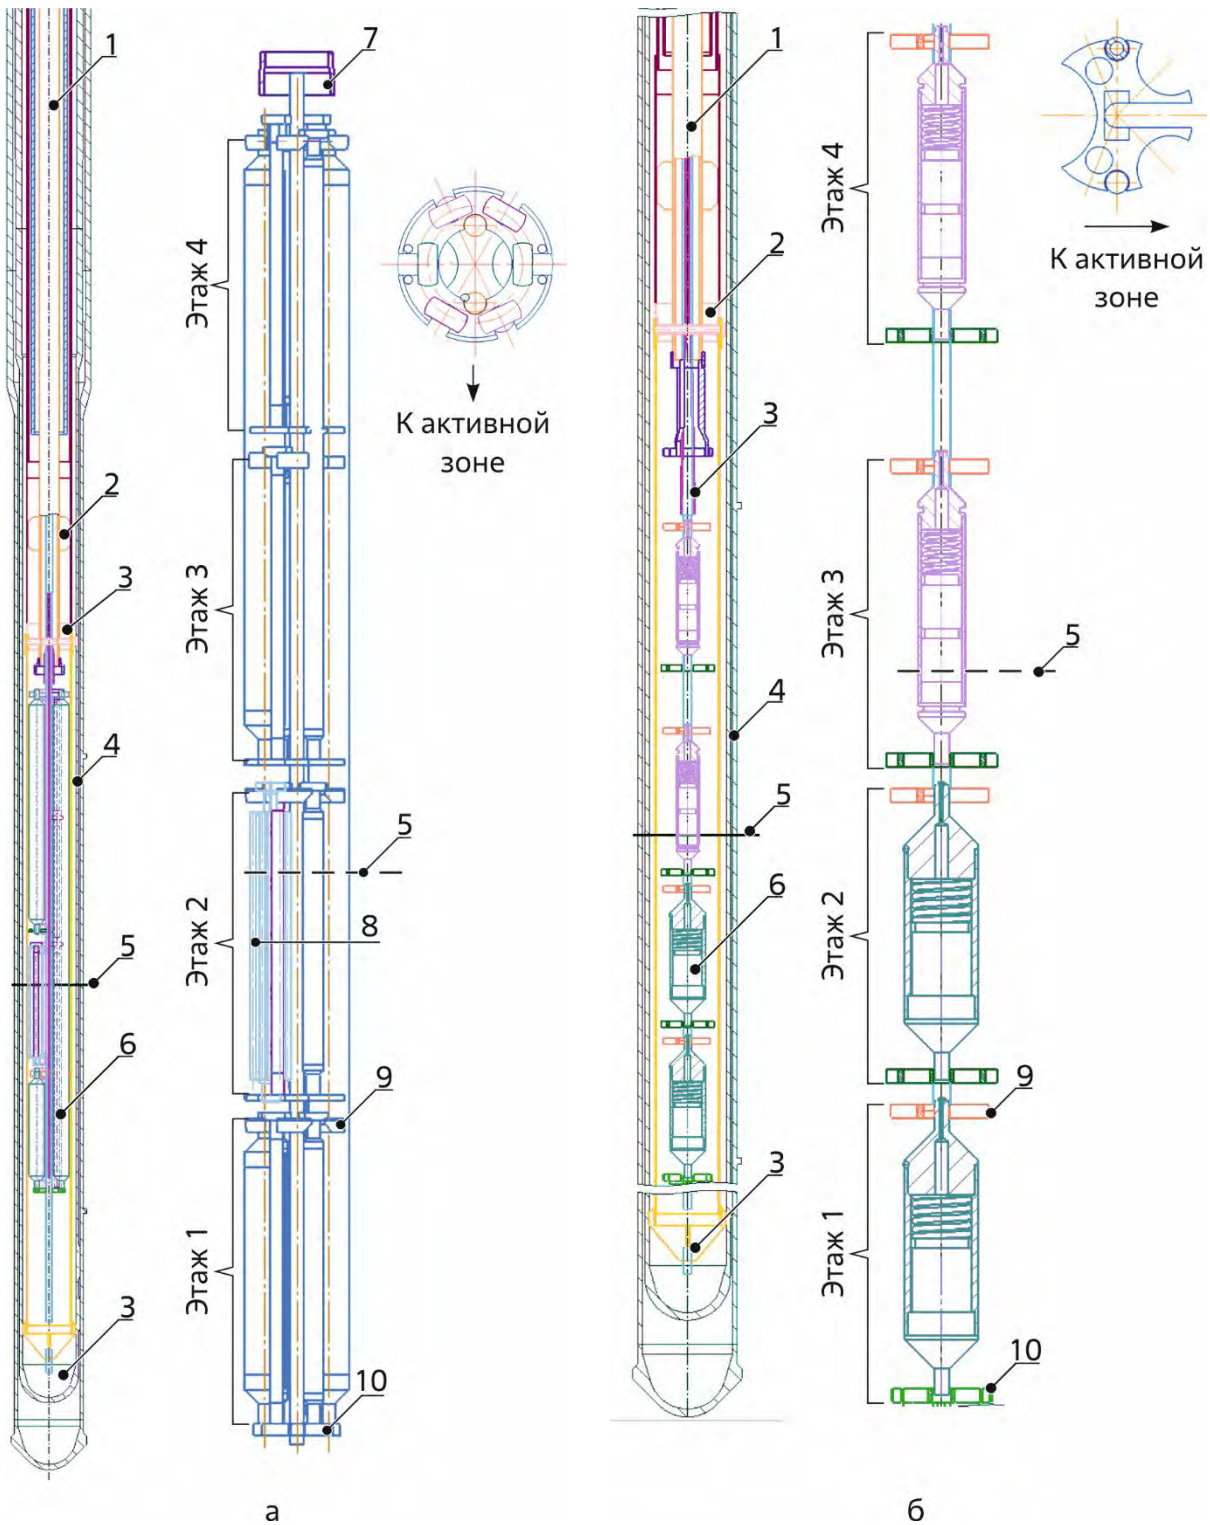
Эскиз и сечения облучательного устройства с макетами нетопливных компонентов (а) и источников нейтронов (б): 1 — несущая труба; 2 — разделитель потока; 3 — термоэлектрические преобразователи; 4 — корпус канала; 5 — центральная плоскость активной зоны; 6 — макеты; 7 — переходник; 8 — вытеснитель потока; 9 — решётка; 10 — удерживающая деталь
